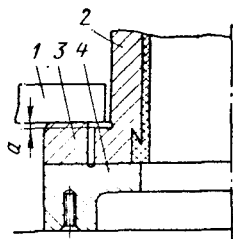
Схема проверки зазора на торце опорной втулки сальника:
